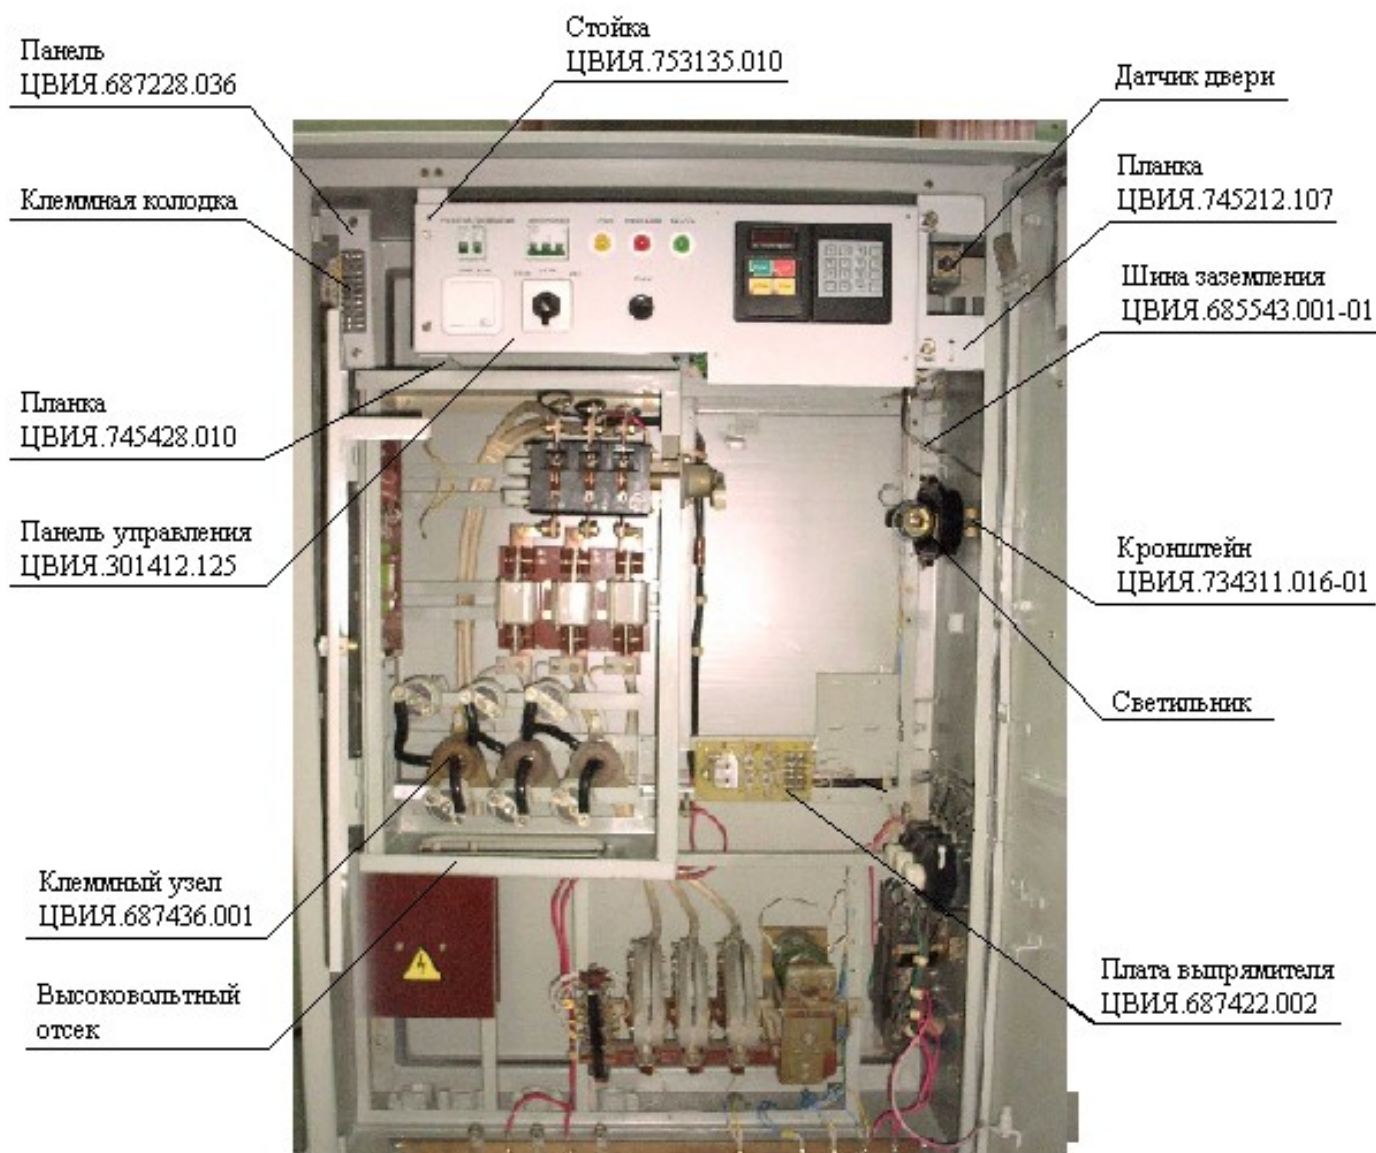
Станции управления ШГС-5805-01 и ШГС-5805-02
